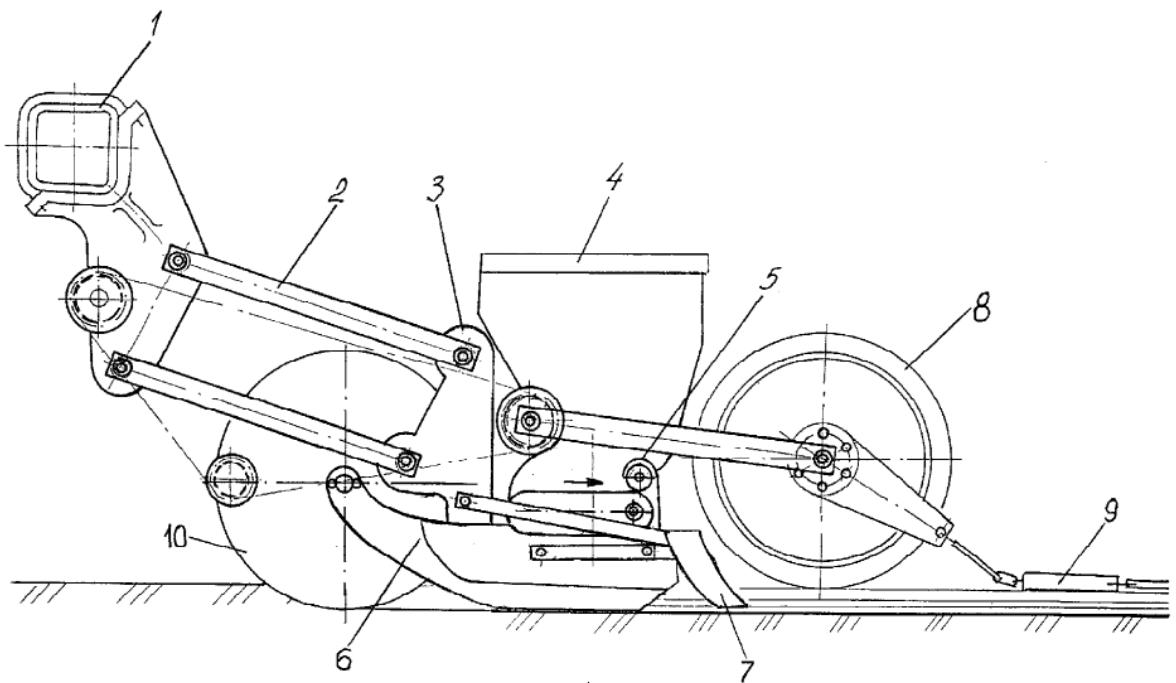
Секция сеялки для разноглубинного посева семян пропашных, бахчевых и крупяных культур: 1-рама; 2-четырехзвенная шарнирно-рычажная система; 3-корпус; 4-семенной ящик; 5-ленточный высевающий аппарат; 6-сошник; 7-загортач; 8-прикатывающее колесо; 9-шлейф
